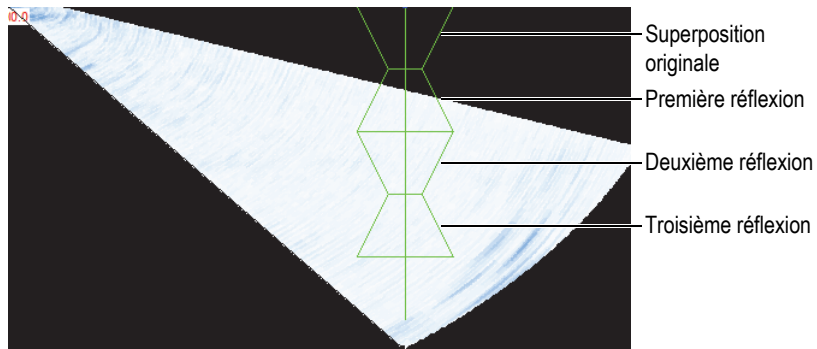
Superposition de soudure incluant trois réflexions
